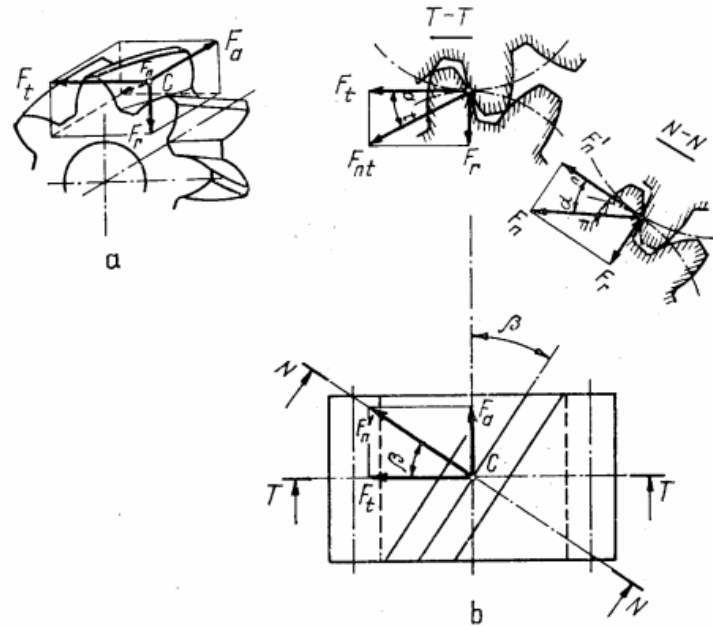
Forces dans un engrenage cylindrique hélicoïdal.
